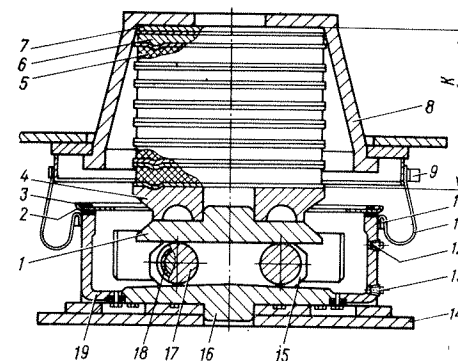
Комбинированная опора: 1, 16 — верхняя и нижняя опорные плиты; 2 — крышка; 3 — болт; 4, 6 — опорные кольца; 5 — упругий элемент; 7 — регулировочные прокладки; 8 — конический стакан; 9, 10 — хомуты; 11 — чехол; 12 — пробка; 13 — сливная пробка; 14 — рама тележки; 15 — обойма; 17 — ролик; 18 — втулка; 19 — корпус роликовой опоры
